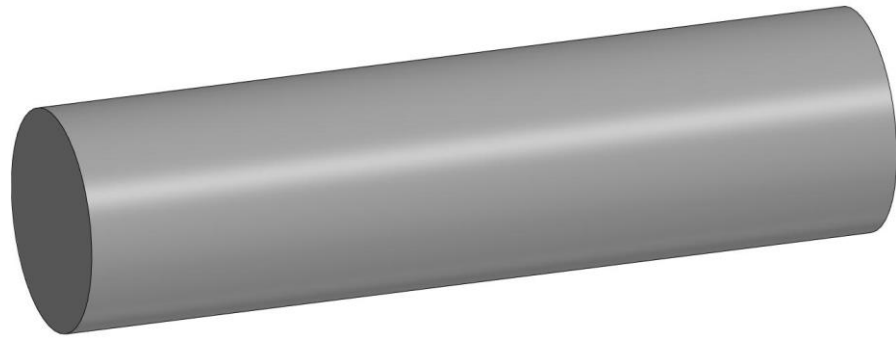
Розрахунок МЦХ заготовки з прутка
